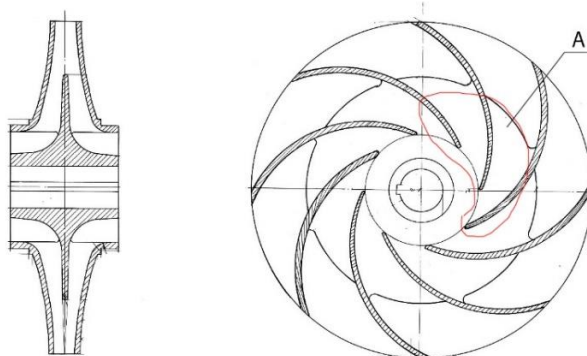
Макет рабочего колеса ТНА для изготовления опытных образцов ЭИ:
